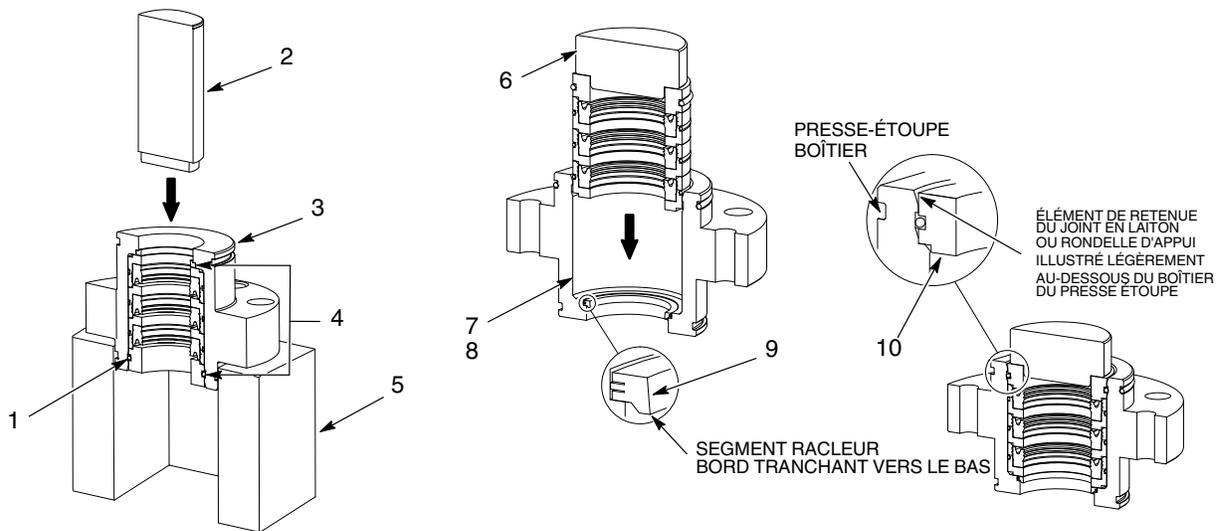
Remplacement des pièces internes du presse-étoupe type
